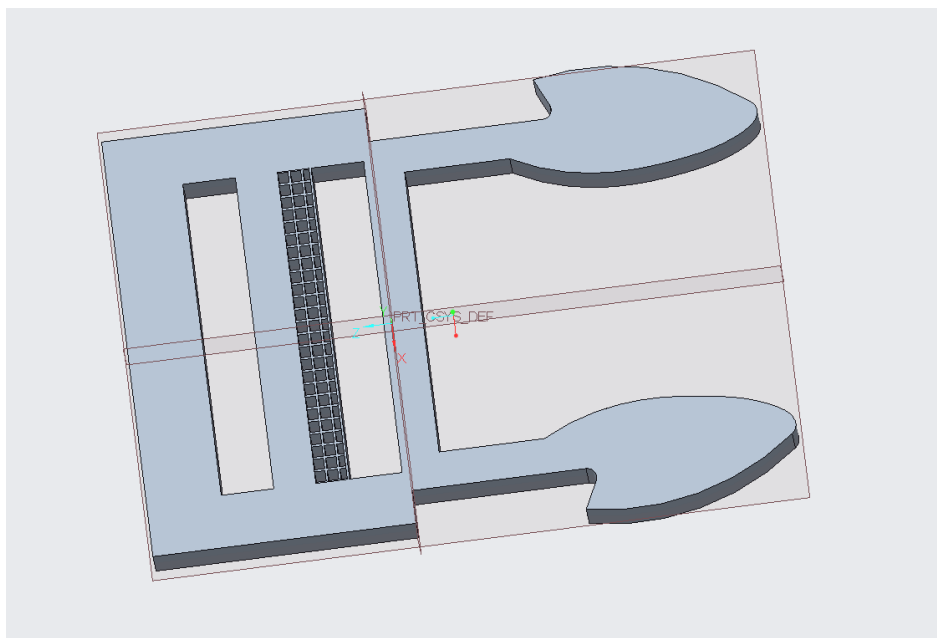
Extrude cut στο κλιπ πόρπης.
